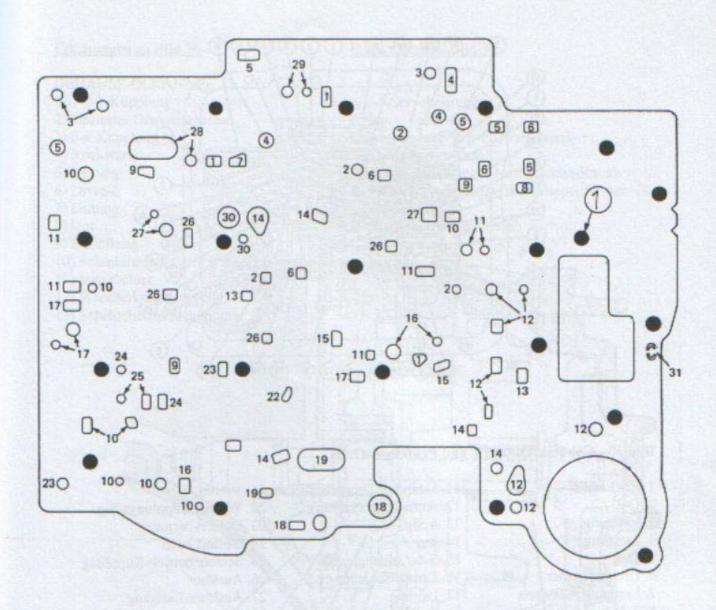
Zwischenplatten-an-Gehäuse-Dichtung
